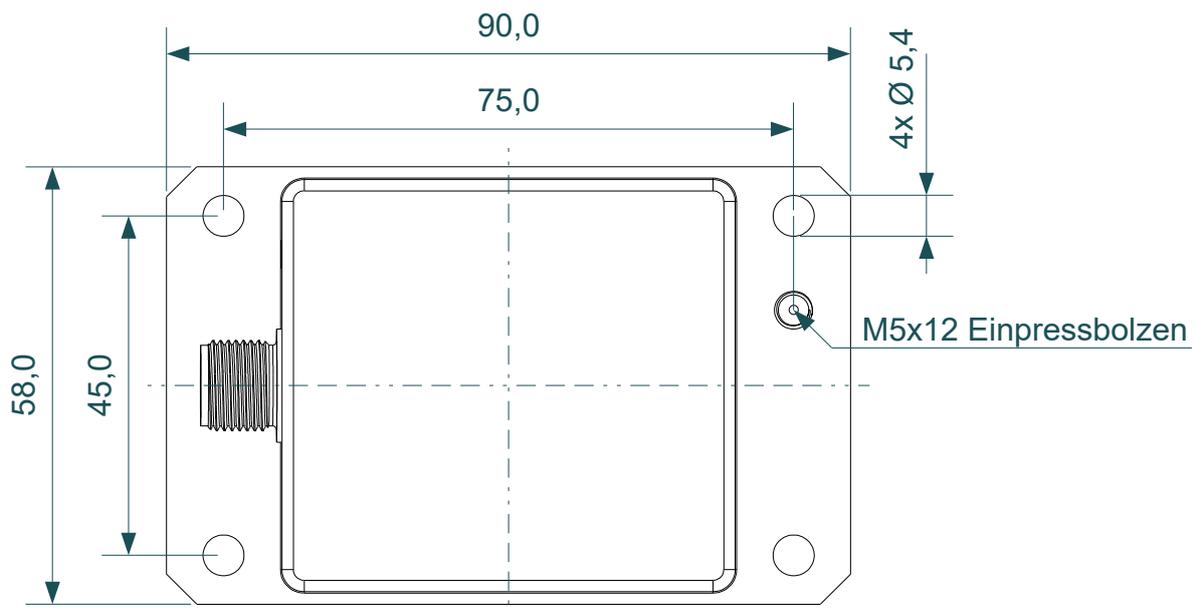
Befestigungsbohrungen Aluminiumgehäuse (MA) (Maße in mm)
